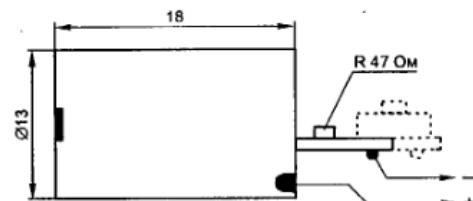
Изготовление из лазерной указки излучателя и его установка
